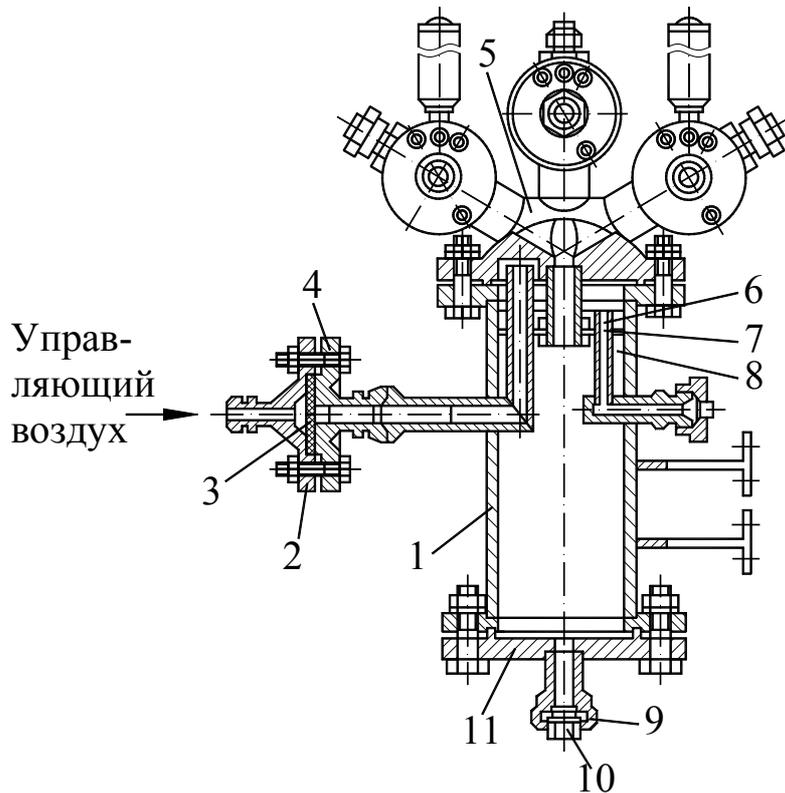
Прибор постоянного давления установки: 1 – корпус фильтра; 2 – крышка клапана; 3 – мембрана; 4 – корпус клапана; 5 – блок камер сгорания; 6 – сливной патрубок; 7 – механический дисковый фильтр; 8 – вода; 9 – гайка; 10 – заглушка; 11 – крышка фильтра.
